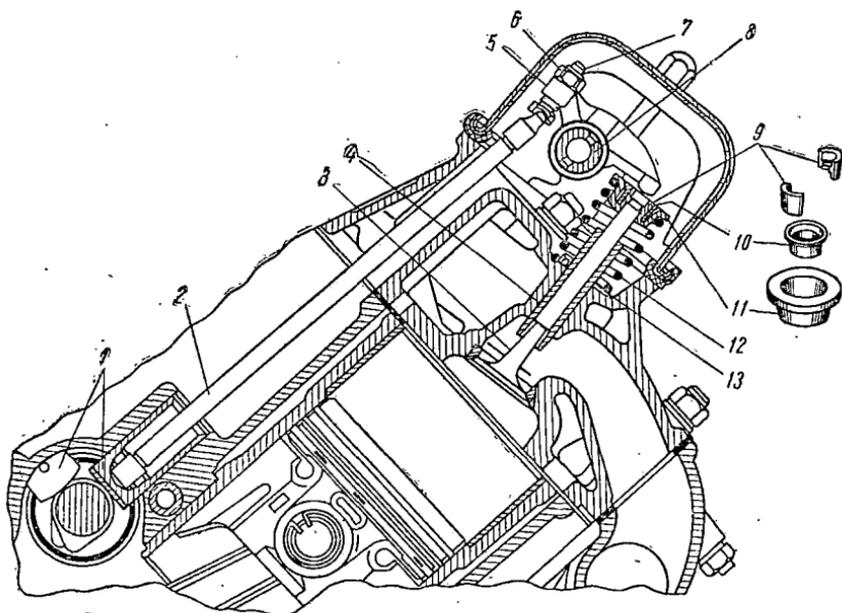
Газораспределительный механизм двигателя ГАЗ-53:
